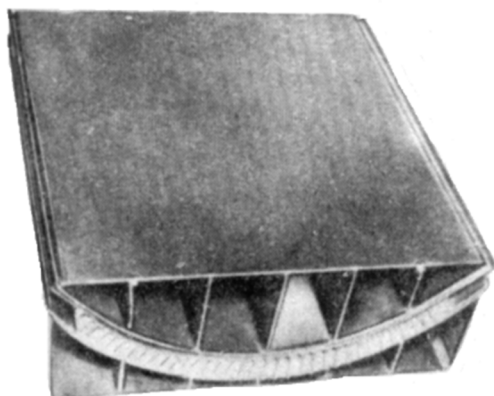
Оснастка для диффузионной сварки сотовой цилиндрической обечайки из сплава ВТ6 с радиусом кривизны 200 мм
